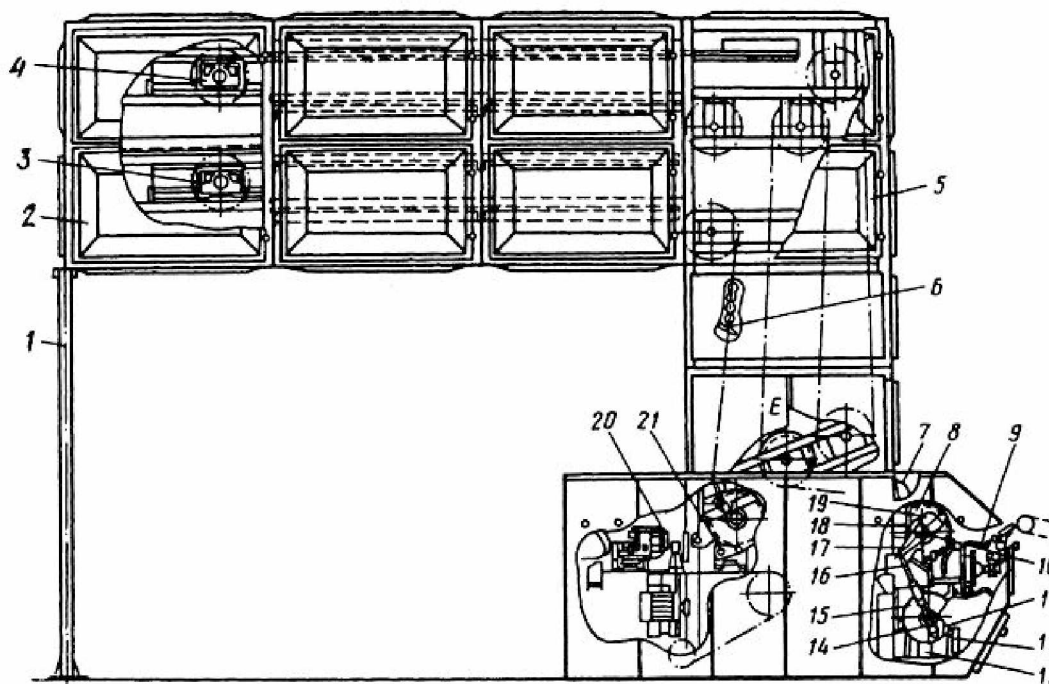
Шафа вистою ЛА-23М: 1 - трубчасті опори; 2 - металеві панелі; 3,4 – пари ланцюгових натяжних зірочок; 5 - ланцюговий конвеєр; 6 - вистійні коліски; 7 - пристрій для регулювання вистоювання; 8 - приводні зірочки; 9 – завантажувач; 10 - ведучий вал; 11, 12 – клинопасові передачі; 13 – електродвигун; 14, 16 - важелі; 15 - черв'ячний редуктор; 17 - поводок храпового механізму; 18 - храпове колесо; 19 – собачка зворотнього ходу храпового механізму; 20 – надрізкач; 21 - перекидач.
